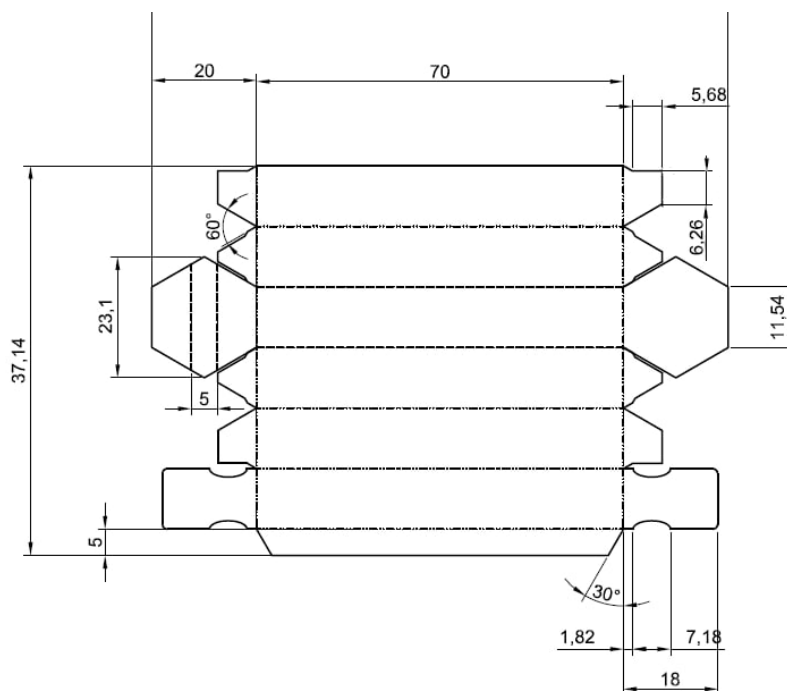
Развёртка упаковки с нанесёнными размерами.
